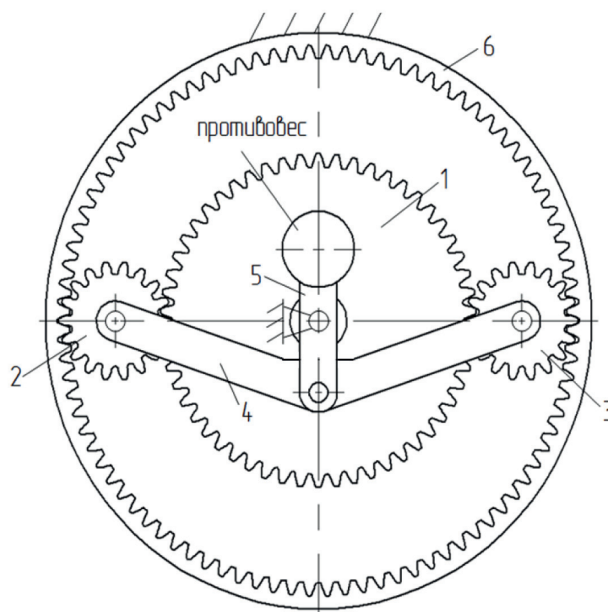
Двухсателлитный планетарный механизм с четырехзвенной группой Ассура
